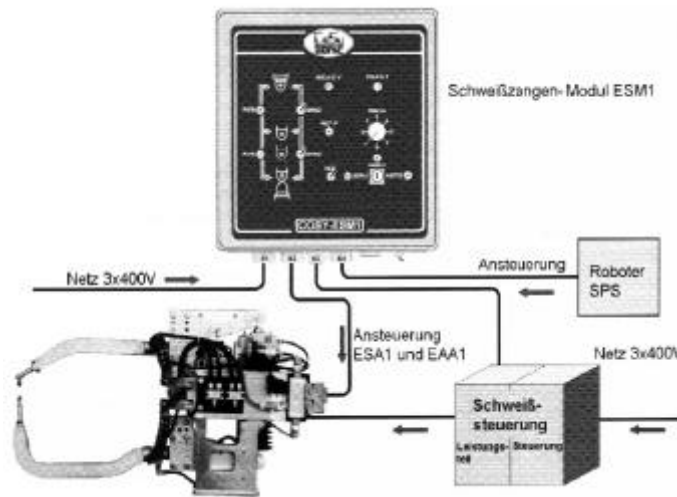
Roboterschweißzange mit Servomotorantrieb und Regelsteuerung; Quelle: Düring Schweißtechnik
